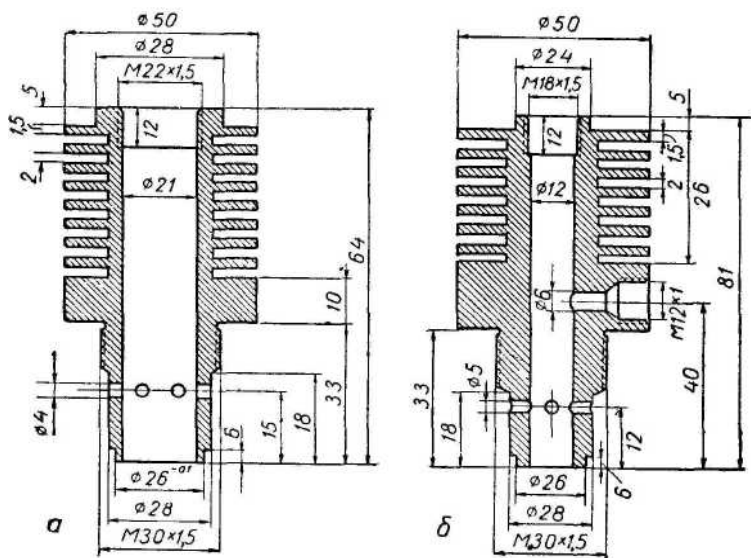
Рабочий чертеж цилиндров: а — второй ступени; б — третьей ступени
